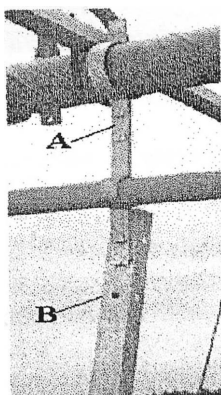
Ilustração de uma braçadeira metálica de aço chato de 1” (A), dando suporte a uma cantoneira metálica (B).
